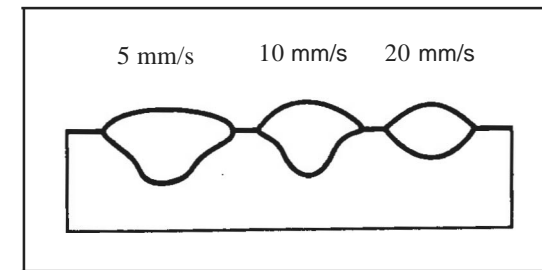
EFECTO DE LA VELOCIDAD DE SOLDEO SOBRE EL ASPECTO DEL CORDÓN
